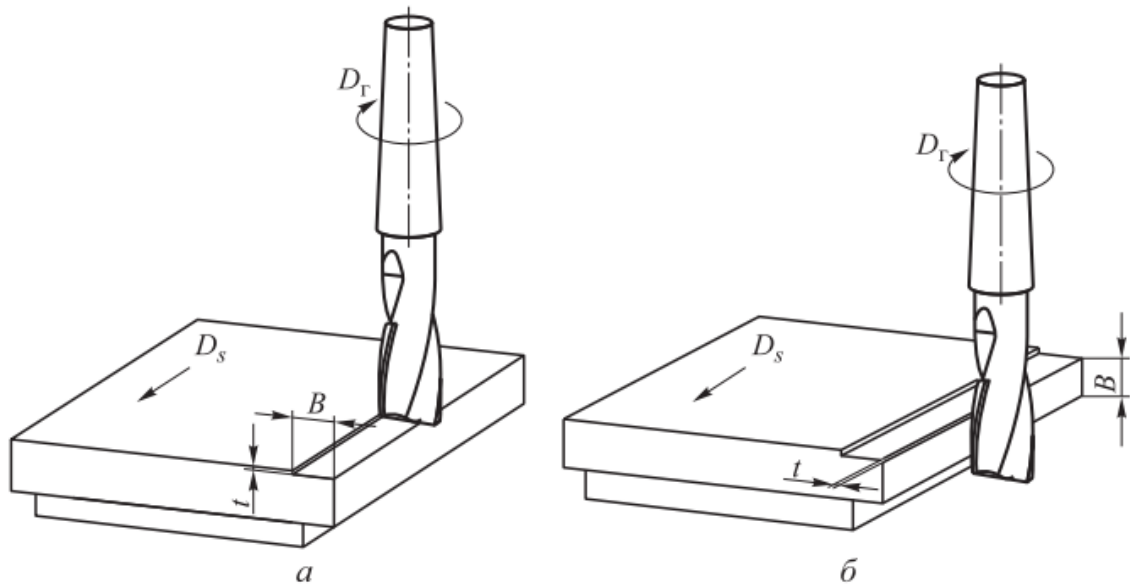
Схеми оброблення плоскої поверхні для торцьового (а) і циліндричного (б) фрезерування
